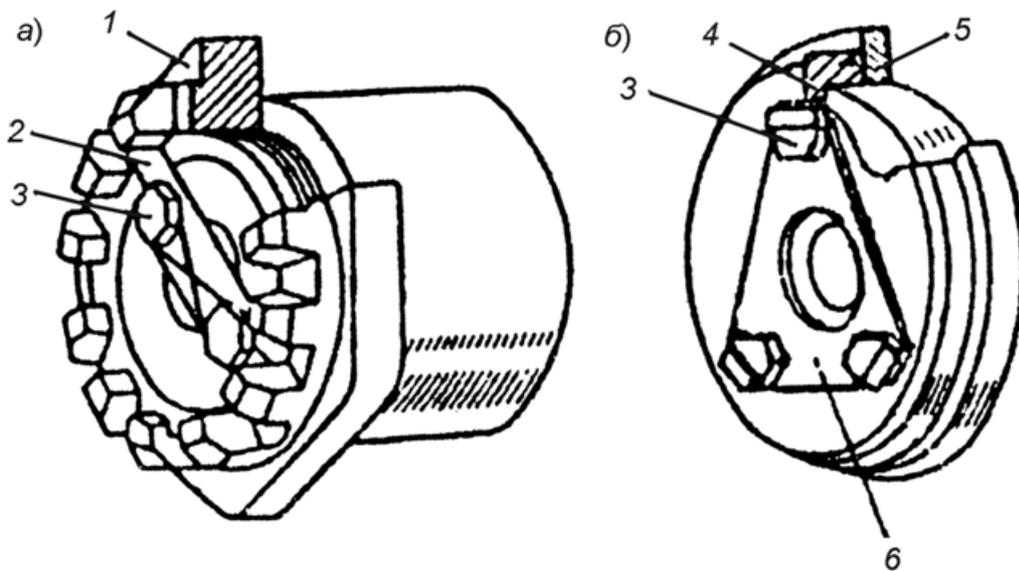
Варианты торцевого крепления подшипников на шейке оси
